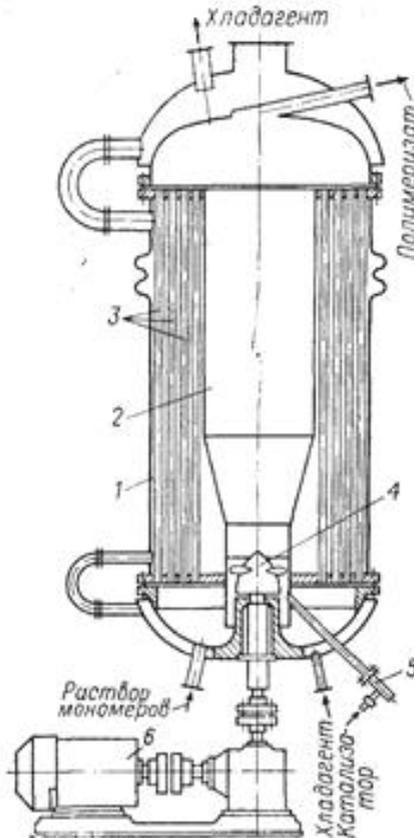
Конструкция реактора-полимеризатора трубчатого типа с диффузором: 1- корпус; 2- центральная циркуляционная труба; 3-трубчатка; 4- лопасти осевого насоса; 5- форсунка; 6- привод
